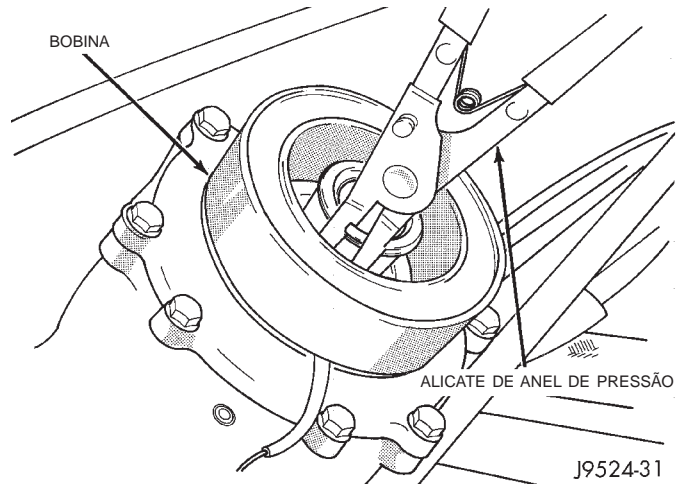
Remoção do Anel de Pressão da Bobina de Campo do Acoplador
